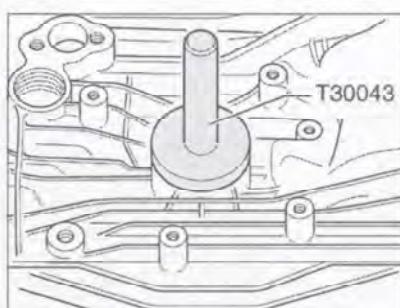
С помощью приспособления T30043 установите новый сальник правого вала на глубину 5.5 мм в корпус коробки передач.
